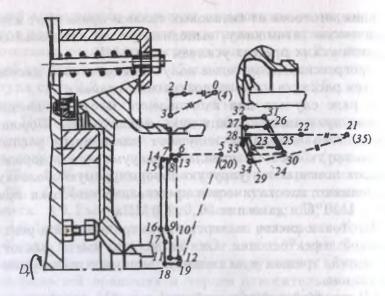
Схема обработки поверхностей диска на токарном станке с ЧПУ
